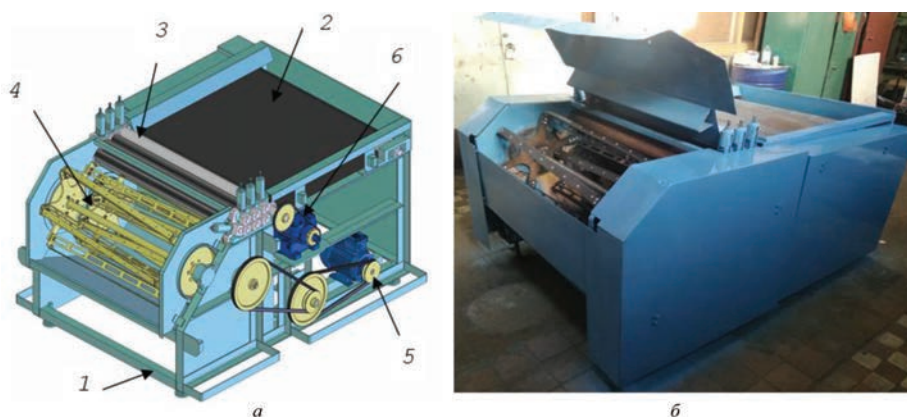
Макетный образец установки трепальной: *а* – 3D модель макетного образца; *б* – общий вид макетного образца:
